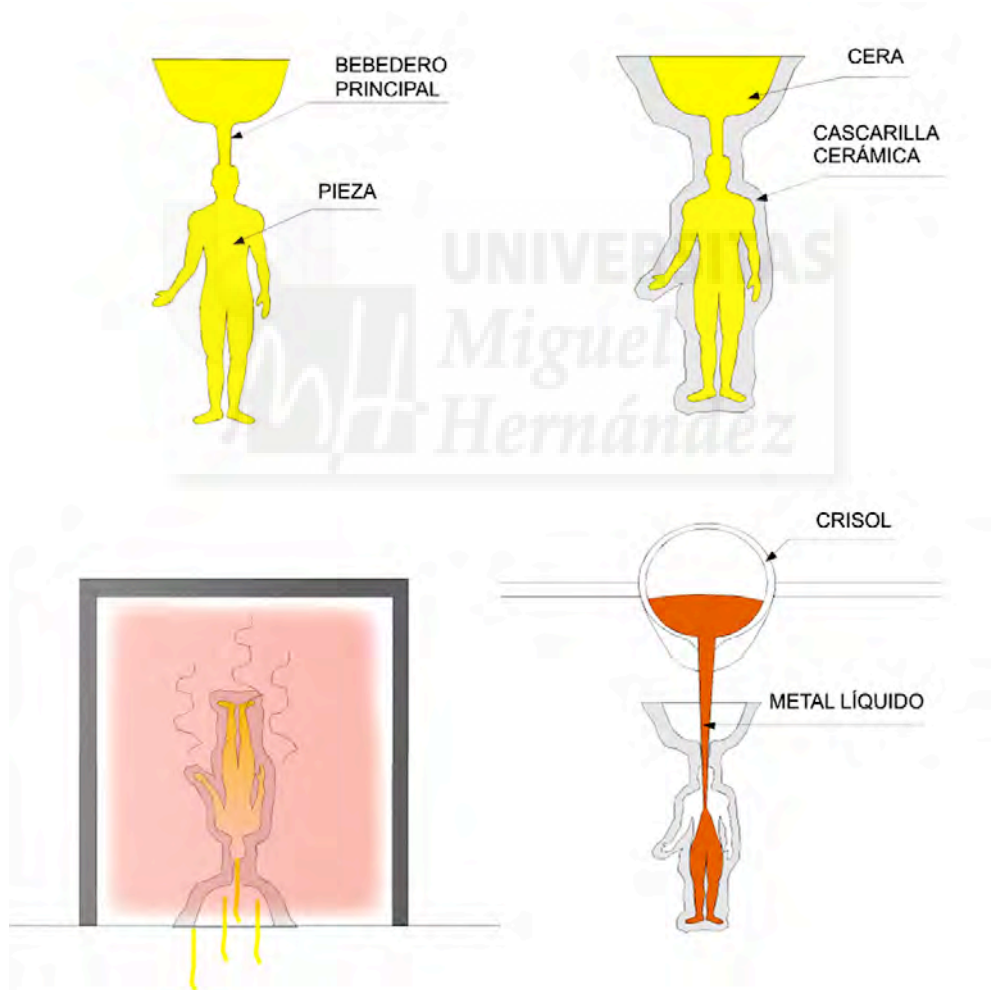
Secuencia de la técnica de la cascarilla cerámica, por Soledad Del Pino.
